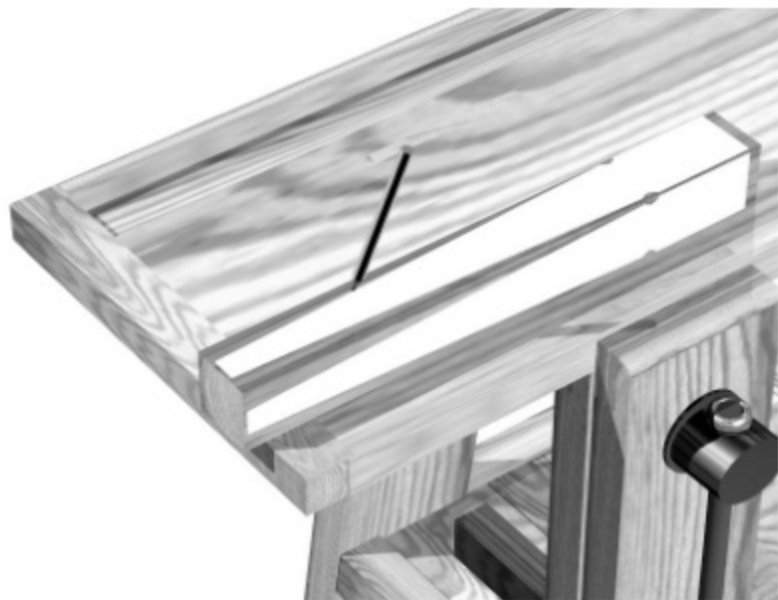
Marcado de la plantilla sobre las dos caras adyacentes de la pata
